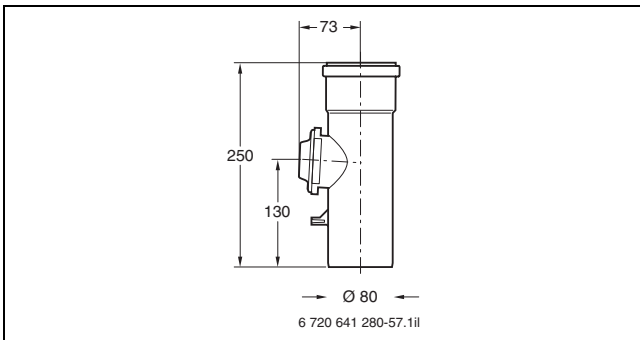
Rohr mit Prüföffnung (Maße in mm)
